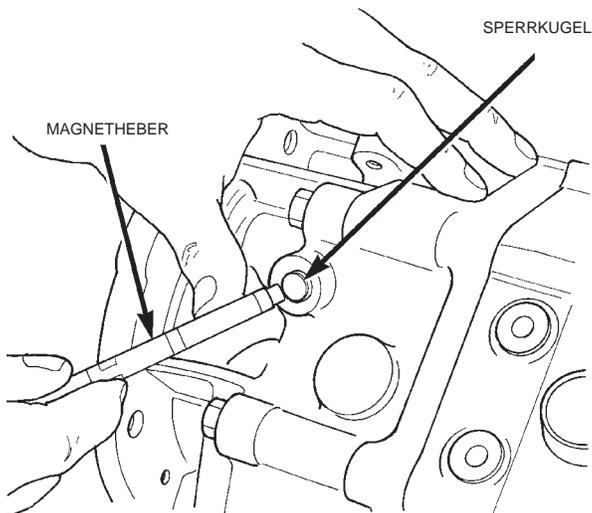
Gewindestopfen der Sperrkugel ausbauen
